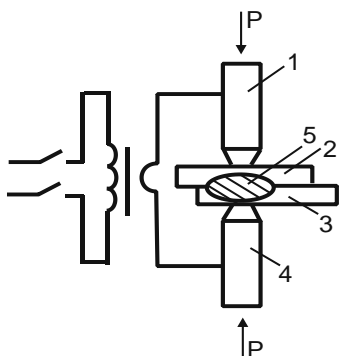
Схема точкового зварювання: 1, 2 – деталі; 3, 4 – електроди; 5 – ядро металу шва
